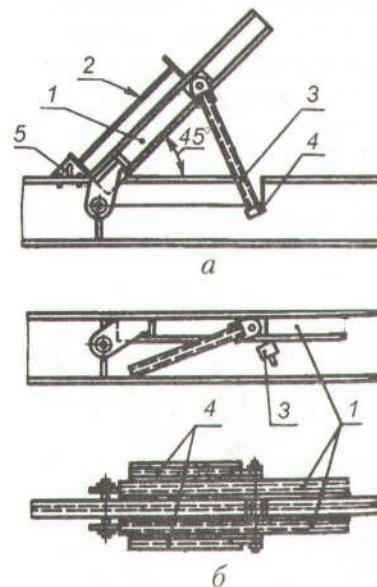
Пристрій для встановлення балок під зварювання:
